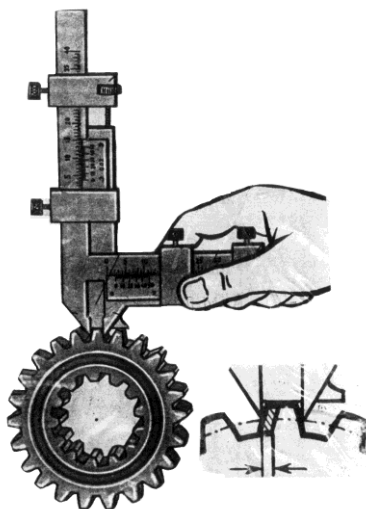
Схема измерения толщины зуба шестерни штангензубомером
